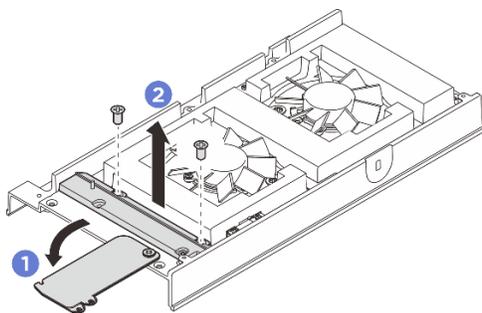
Extracción de la cubierta de cables del puente del ventilador
